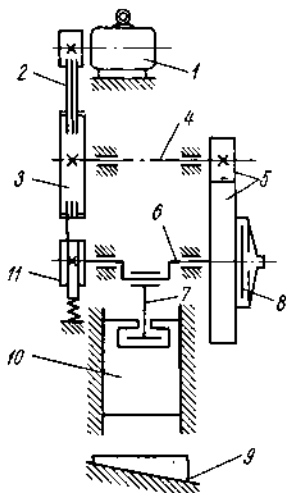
Кинематическая схема кривошипного горячештамповочного прессы
